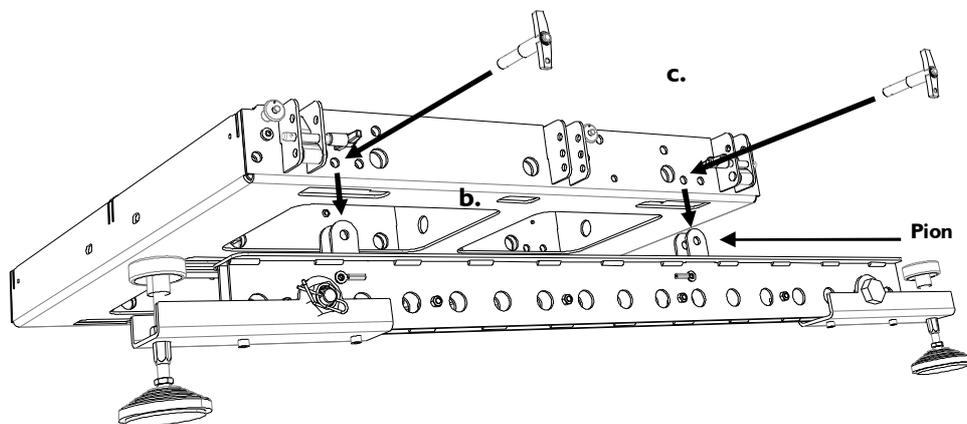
Montage de la plateforme (exemple en extension arrière)
